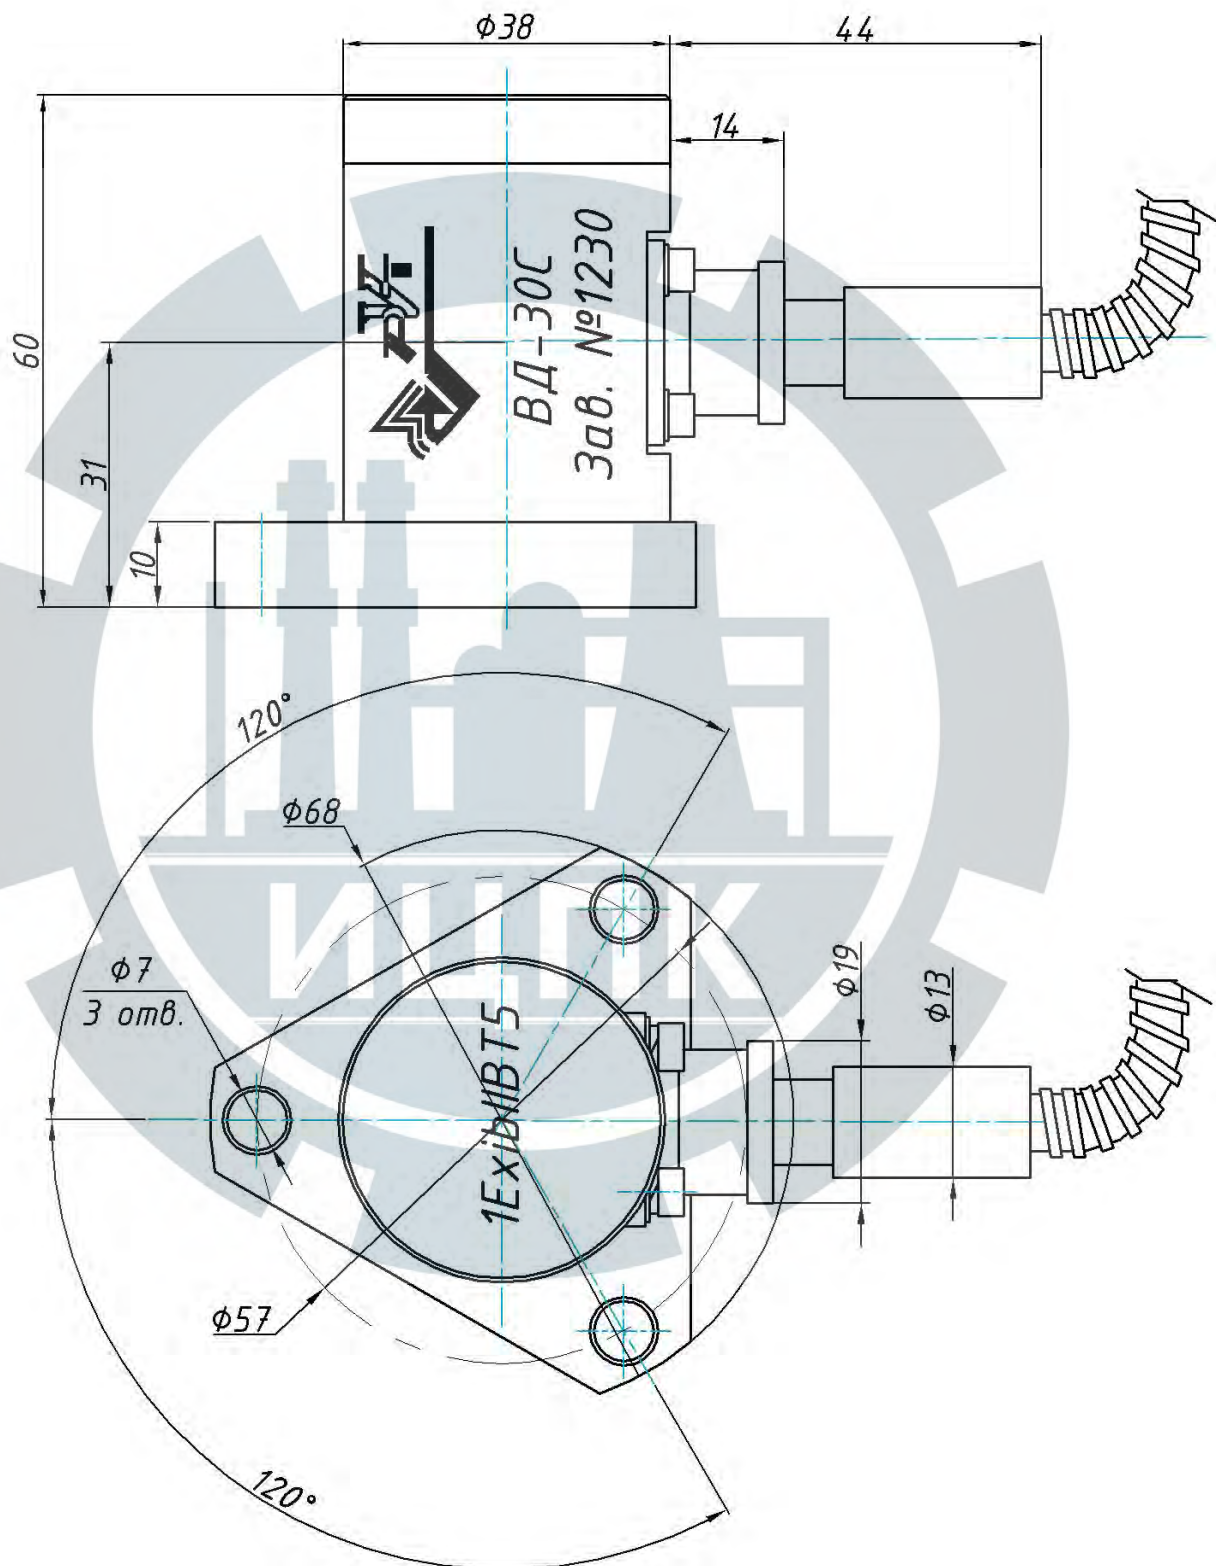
Габаритные и установочные размеры ВД-30С.01-3
